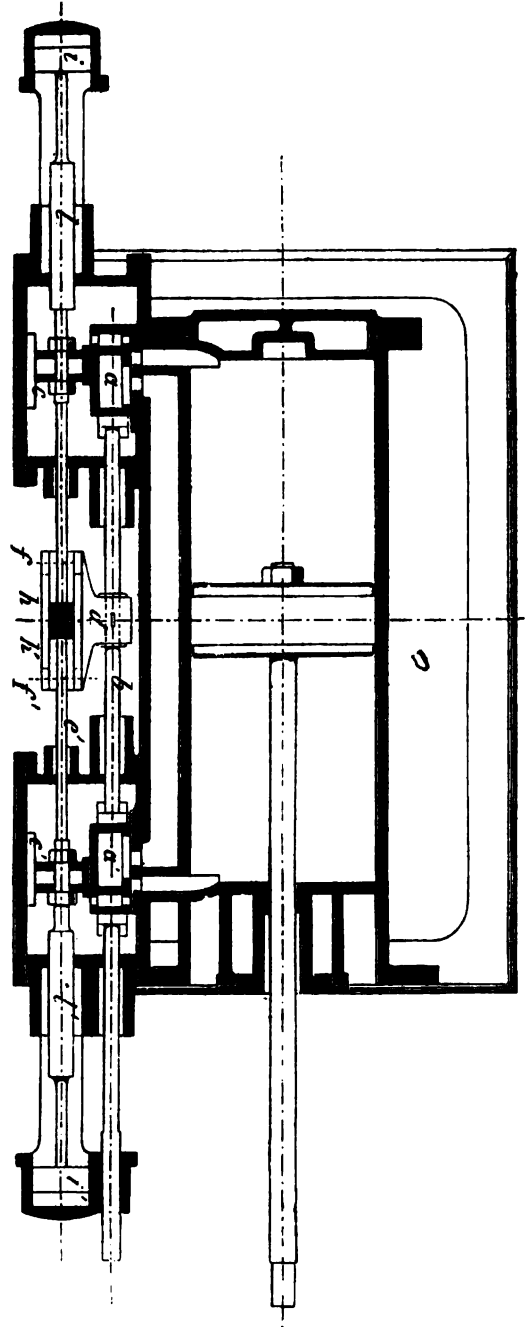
$\Sigma$  Horizontaler Mittelschnitt der Dampfmaschine mit Gleichlaufsteuerung.
